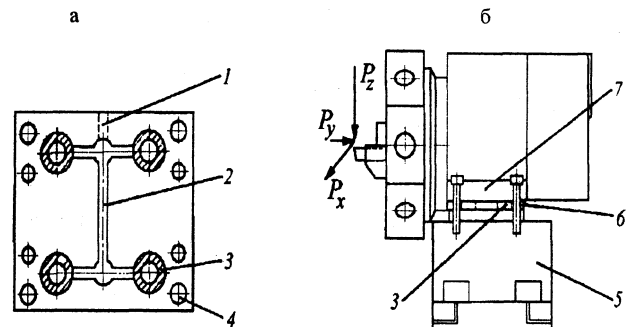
Измерительная плита на основе комплекта пьезоэлектрических элементов: а – продольный разрез; б – схема установки на станке; 1 – соединительный кабель; 2 – каналы для кабеля; 3 – пьезоэлектрические элементы; 4 – отверстия под крепежные винты; 5 – поперечный суппорт; 6 – измерительная плита; 7 – основание револьверной головки
